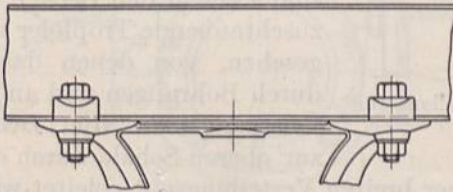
Befestigung der Lager mittels Klemmplatten.
